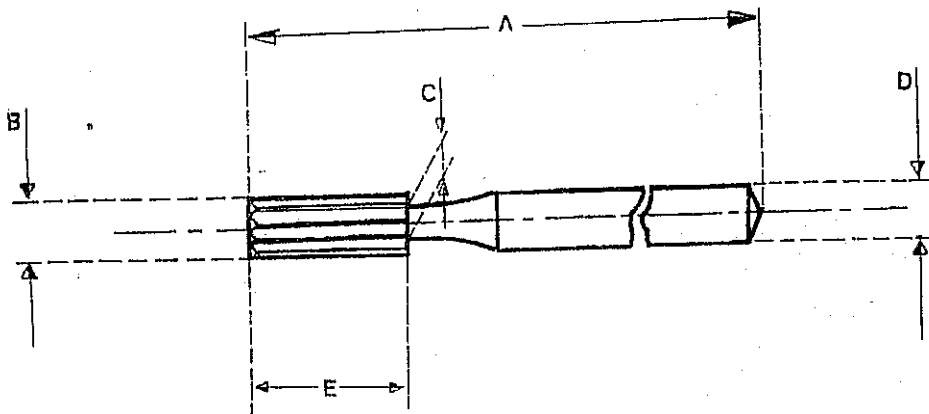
Fresas de carburo, forma cilíndrica (claves: 060.431.0441, 060.431.0636, 060.431.0664)
